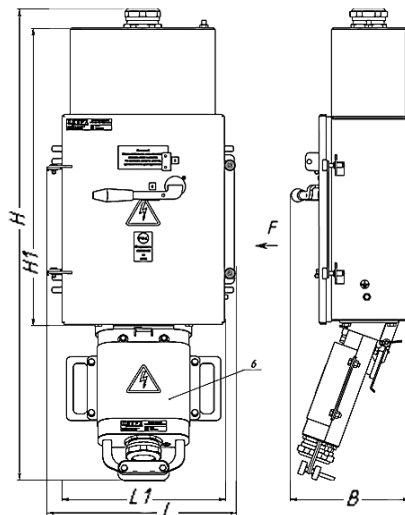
Общий вид и габаритные размеры ВРН-Ш/Р(Twin) 630 А
